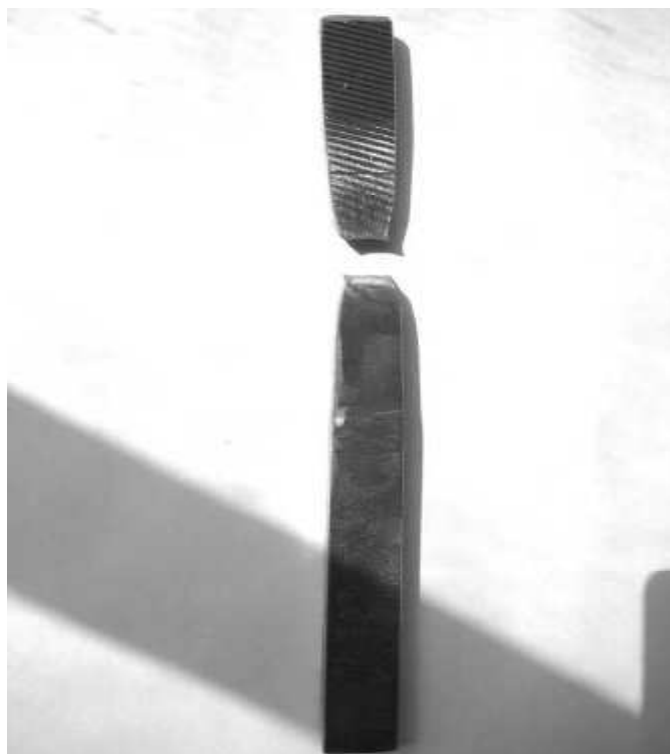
Образец WELDOX 700E + 09Г2С
